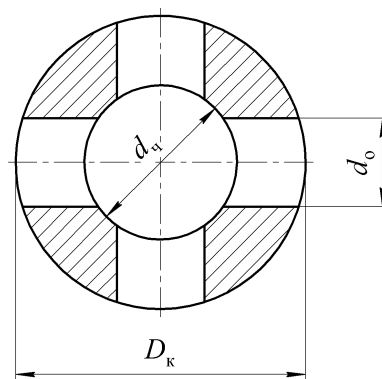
Розрахункова схема небезпечного перетину корпусу вантажного гвинта 2-го типу.
